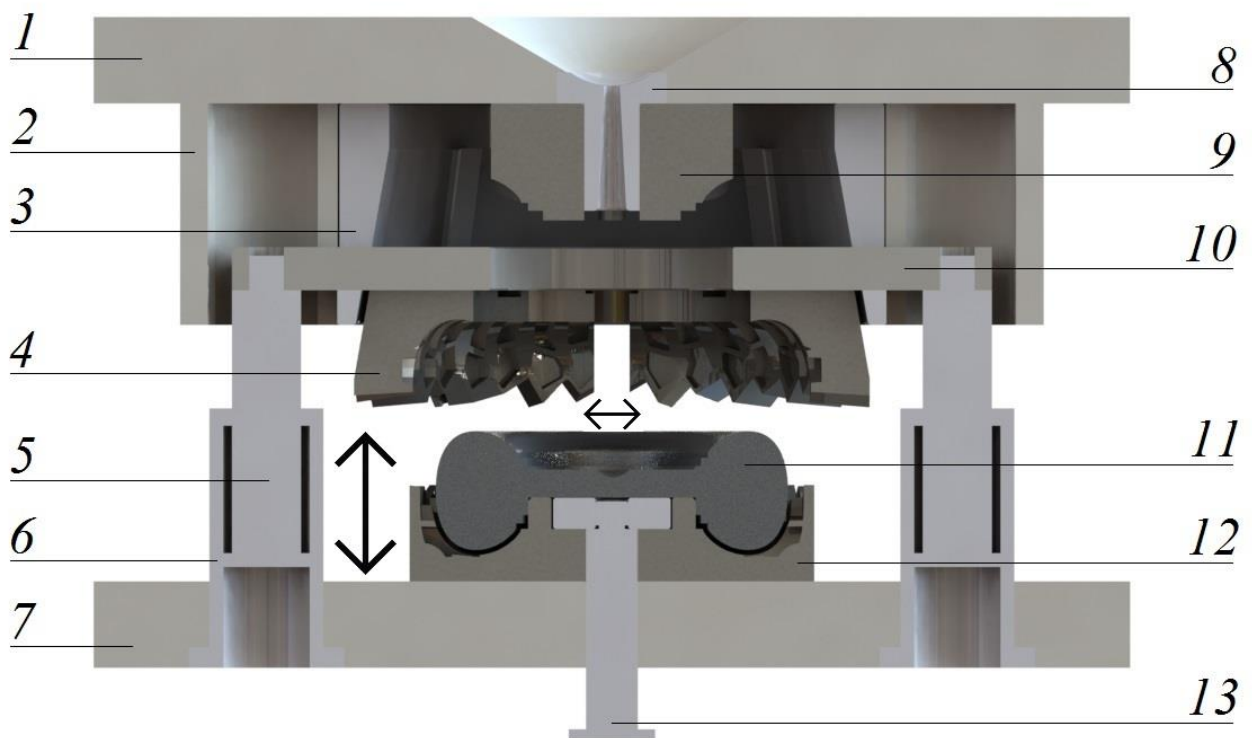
Модель одномісної прес-форми для виготовлення гумового колеса для радіо моделей (1 – нерухома плита форми; 2 – проміжна плита; 3 – напрямна втулка рухомої пів-матриці; 4 – рухома пів-матриця; 5 – колонка; 6 – втулка; 7 – рухома плита форми; 8 – нерухома ливникова втулка; 9 – пів-матриця; 10 – рухома плита пів-матриці; 11 – вкладиш; 12– нерухома матриця; 13– знімач)
